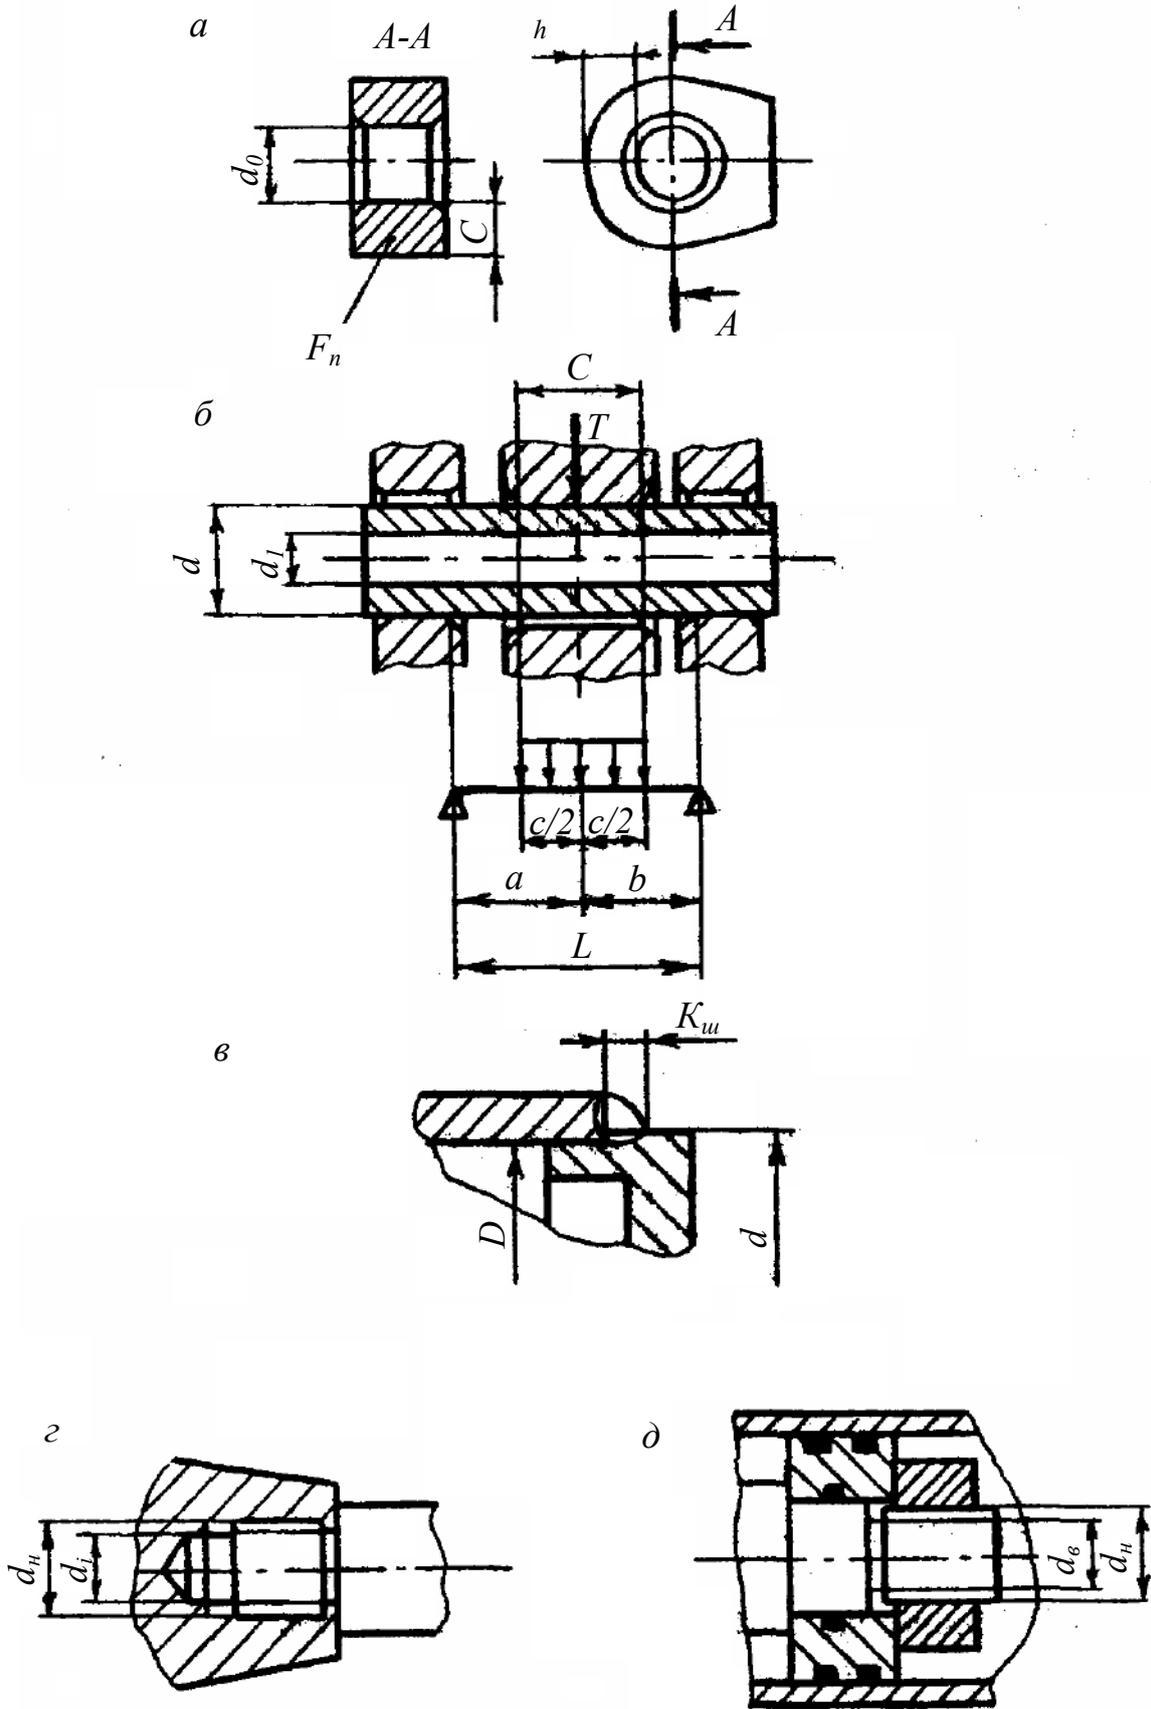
Расчетные схемы проушины, пальцев, сварных швов и резьб
